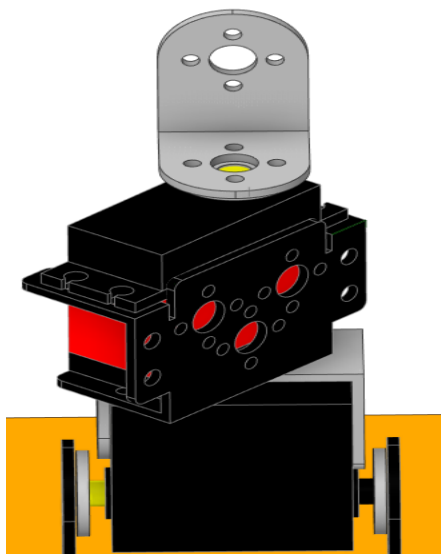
Výsledné uchycení servomotoru k držáku
